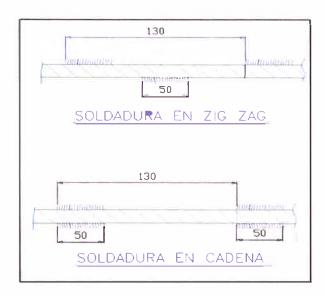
Soldadura Zig - Zag y Cadena
